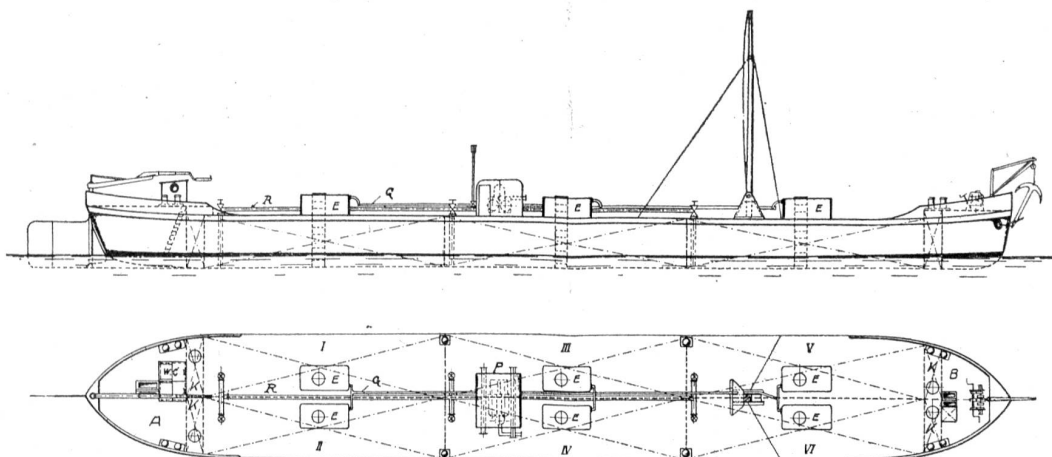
Längsschnitt und Grundriss eines Kanalschiffes.
